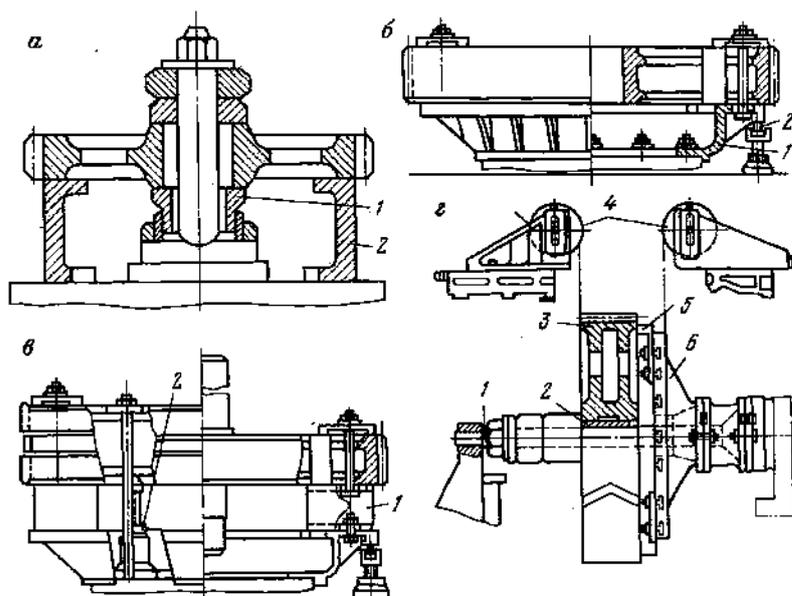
Типовые схемы установки заготовок (крупногабаритных) зубчатых колес на зубофрезерных станках:
